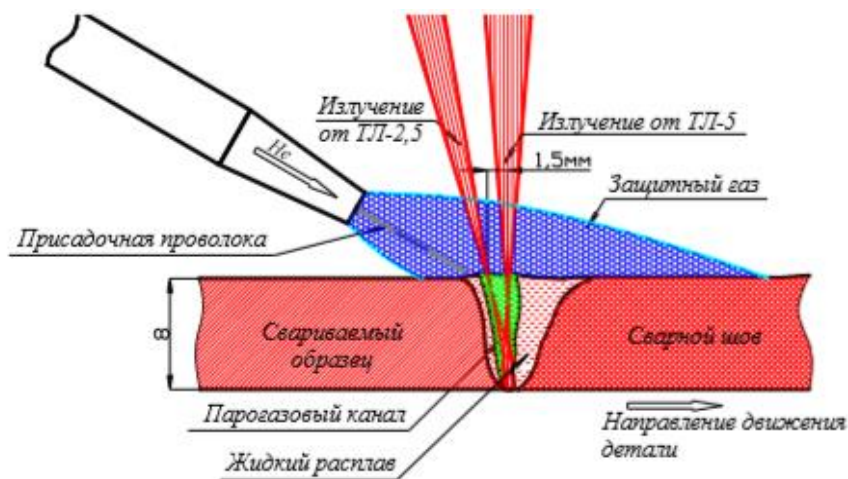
Схема двухлучевой лазерной сварки
